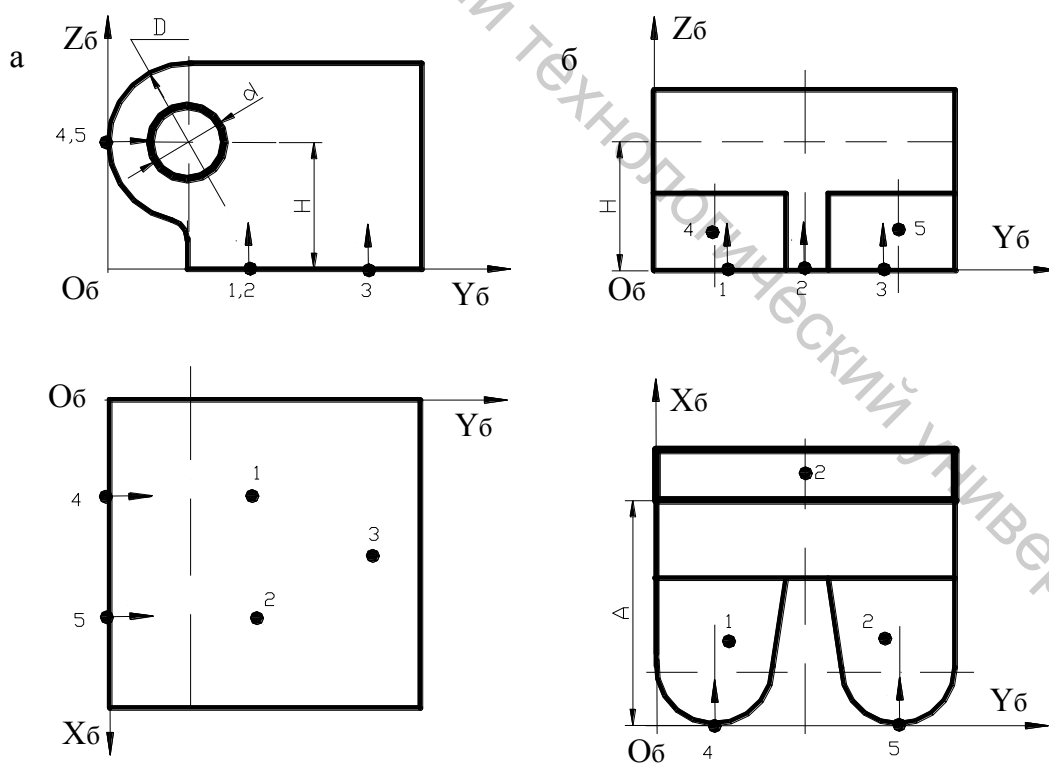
Схема реализации направляющей базы с помощью: образующей цилиндра (а), образующими двух наружных цилиндров (б)
